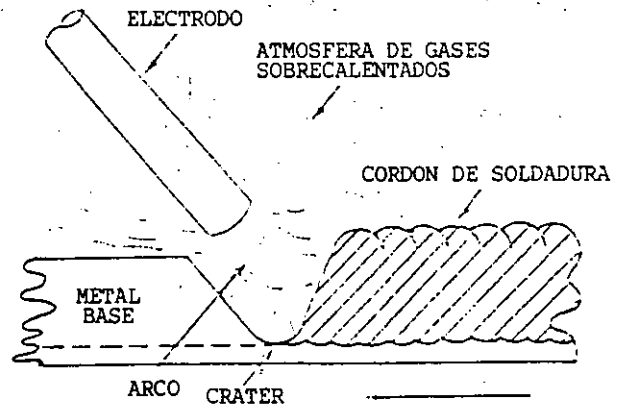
FIG. _____ SOLDADURA DE ARCO DE UN ELECTRODO DESNUDO EN PROCESO
